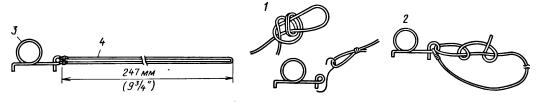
Подготовка тросика сервопривода индикаторной пленки и регулировки громкости: I — завизывание узла, 2 — оба конца тросика надеваются на пружину натяжения, 3 — пружина натяжения тросика; 4 — тросик диаметром 0.5 мм
